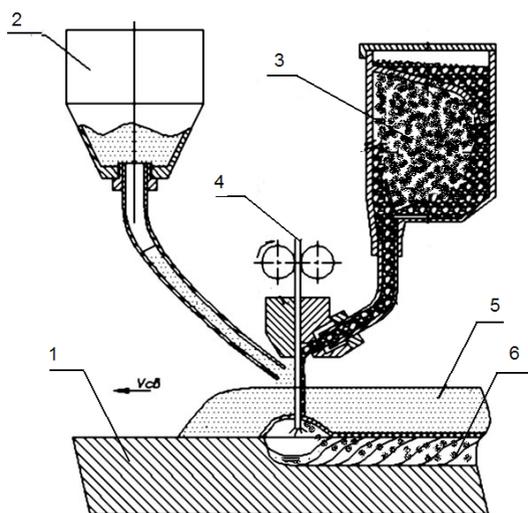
Схема процесса сварки с подачей ППМ на вылет электрода:
